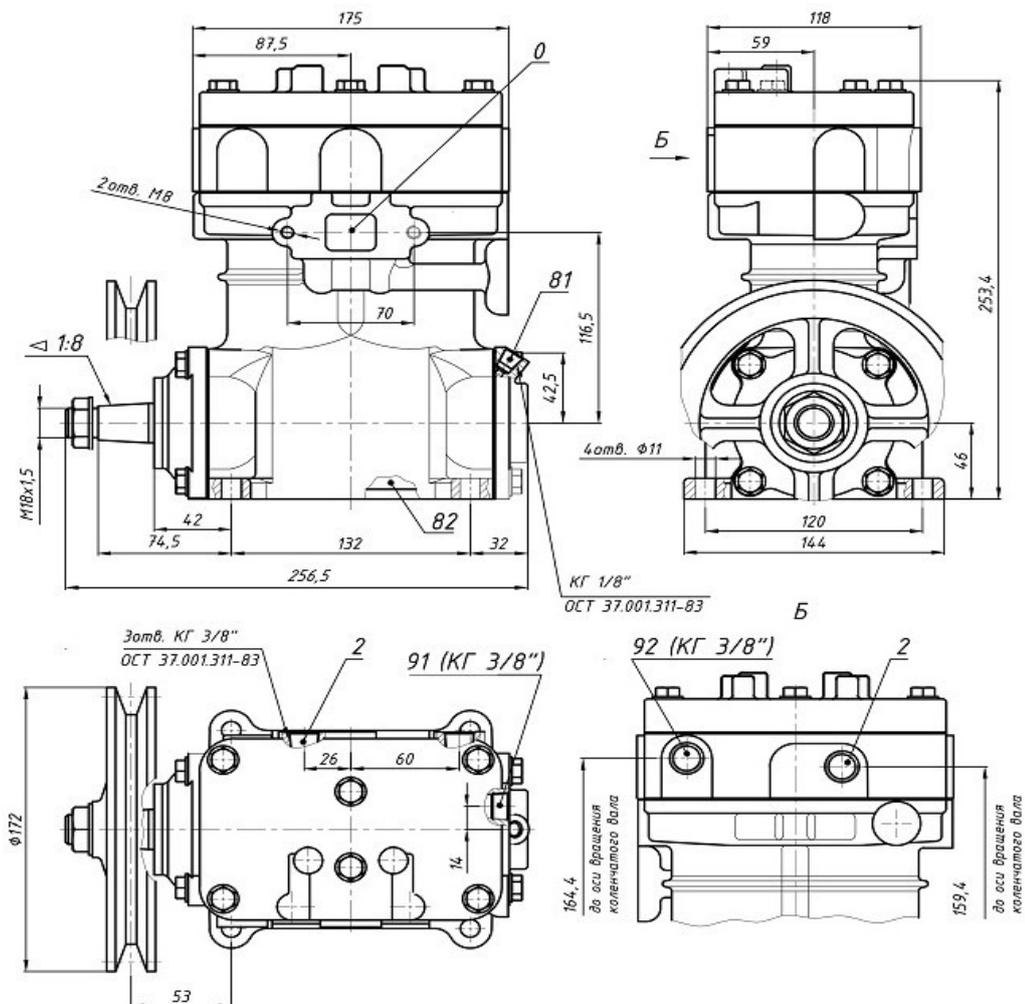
Присоединительные и установочные размеры компрессора АМ.3509012-16.
